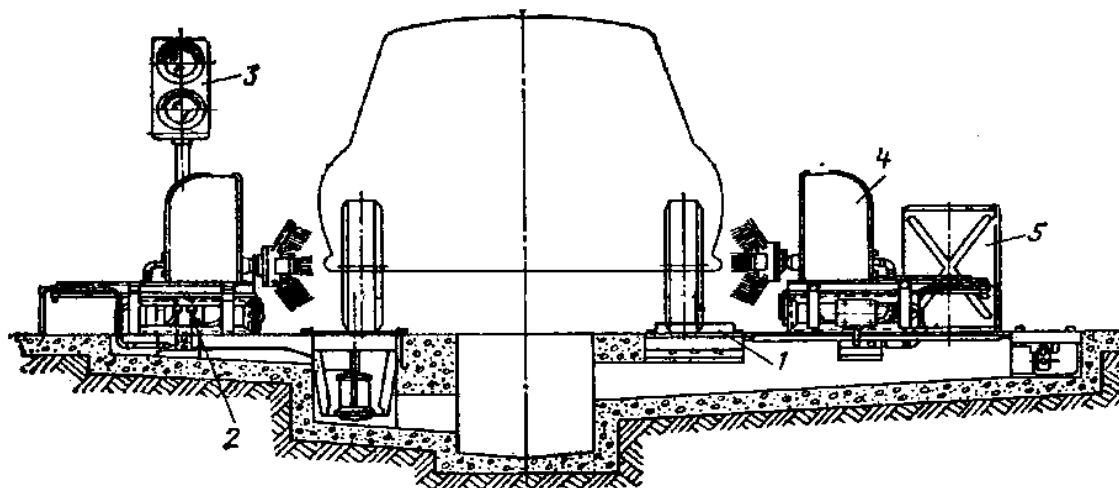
Установка для мойки колёс легковых автомобилей:
